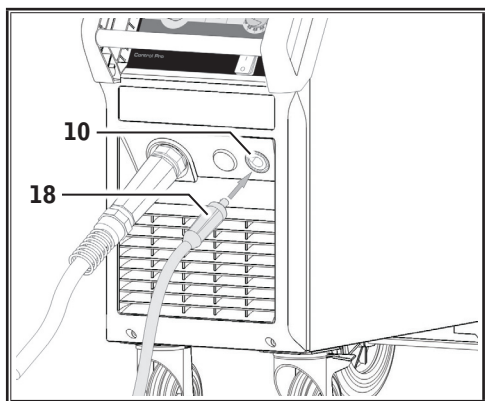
Подключение кабеля для заземления обрабатываемой детали
